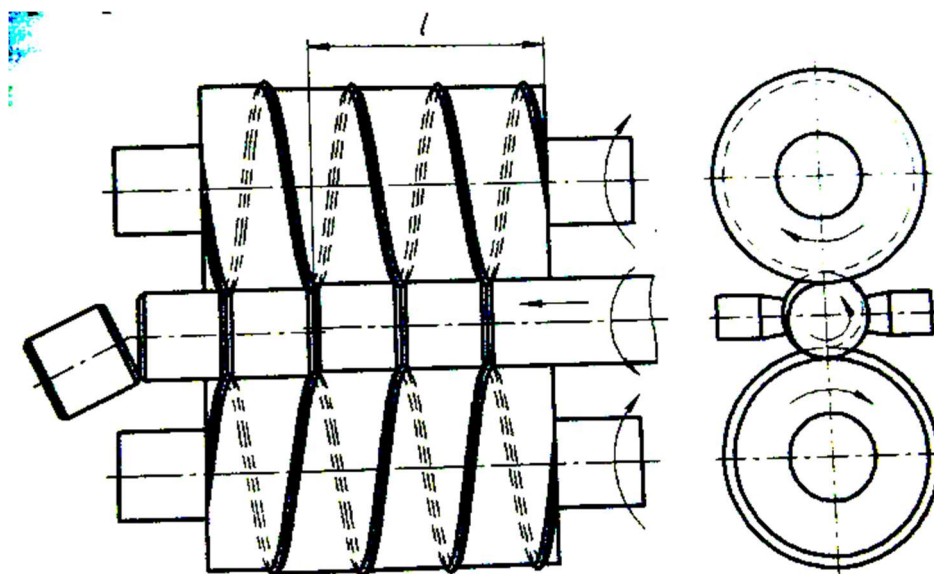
Схема разделения прутка на заготовки винтовой прокаткой
